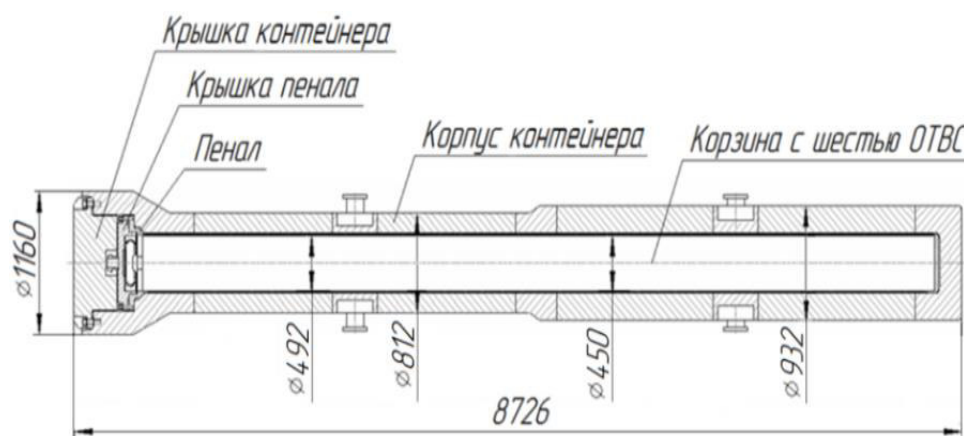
Схема конструкции ТУК [TPS constructional scheme]
